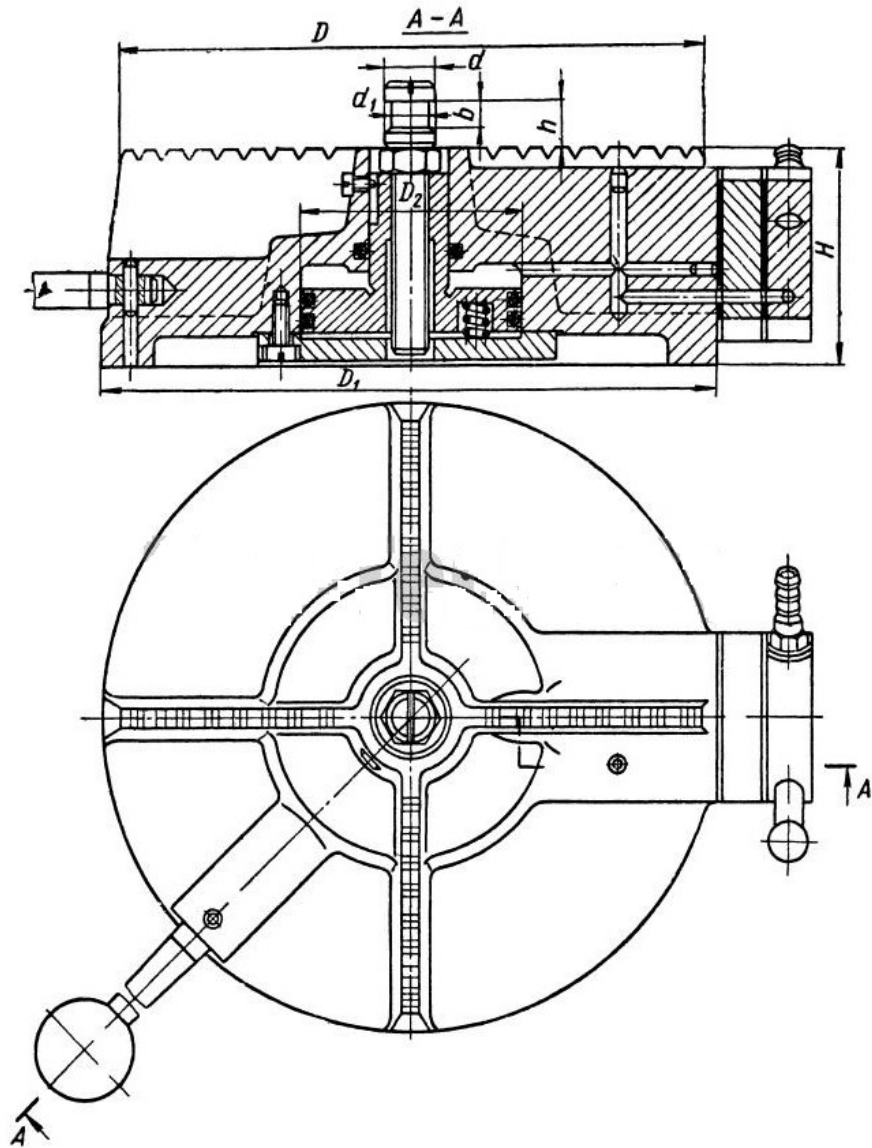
Підставка універсальна для накладного кондуктора з пневмоприводом
